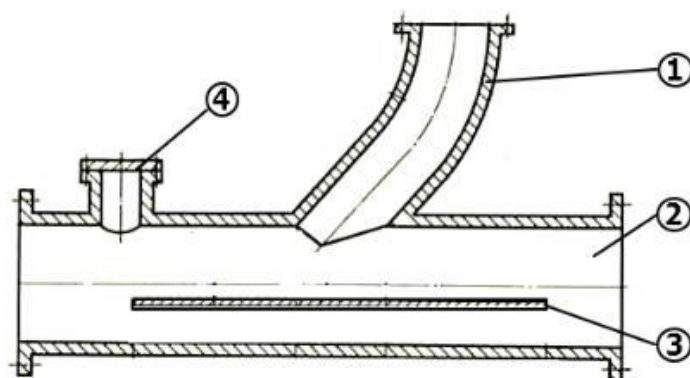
Загрузочное устройство типа тройник пневматического транспортера
